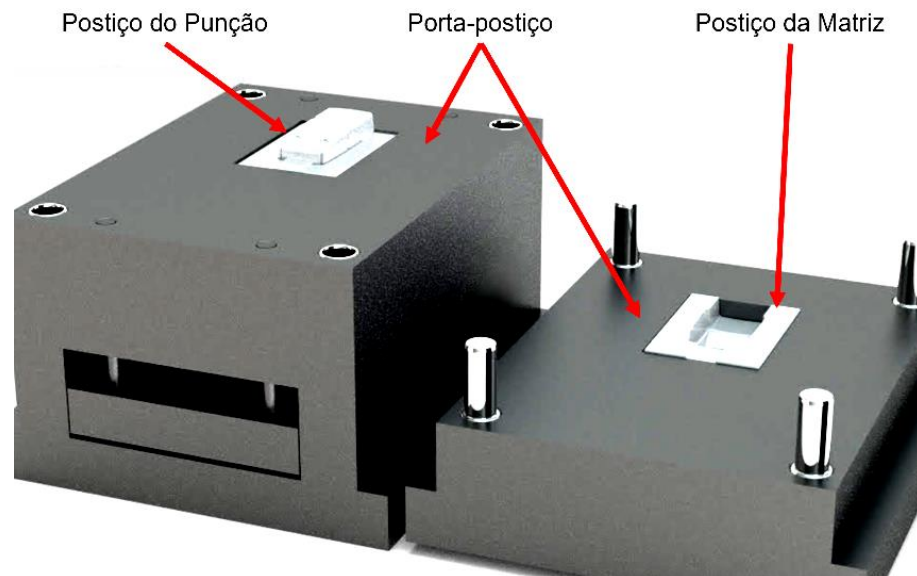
Cavidades moldantes de resina alojada no porta-postiço de aço.
